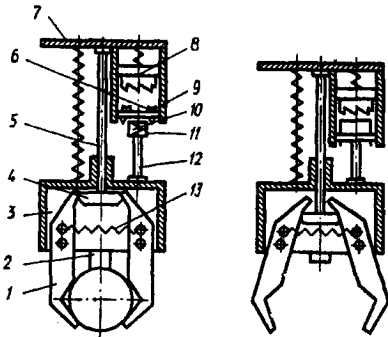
Механічний захватний пристрій із стопорним механізмом: 1 – губки; 2 – упор; 3 – головка; 4 – замикаюча планка; 5 – направляюча; 6 – зубці храповика; 7 – корпус; 8 – верхня втулка; 9 – нижня втулка; 10 – виступи клямки; 11 – засочка; 12 – вісь клямки; 13 – пружина
